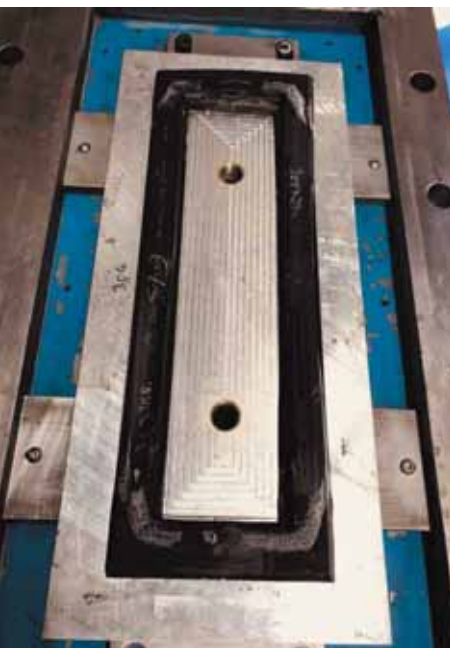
Стенд для выполнения лабораторных испытаний на герметичность уплотнителей
